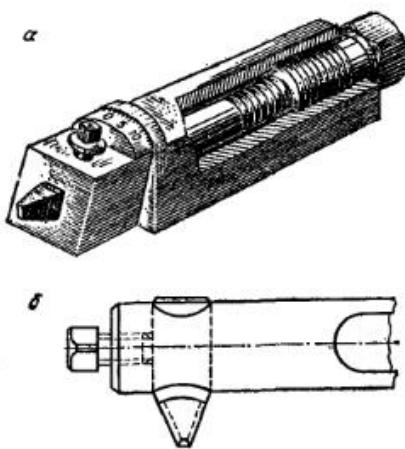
Державки для поворота резьбовых резцов на угол подъема: а — с поворотной головкой; б — оснащенной резцом с круглым стержнем
